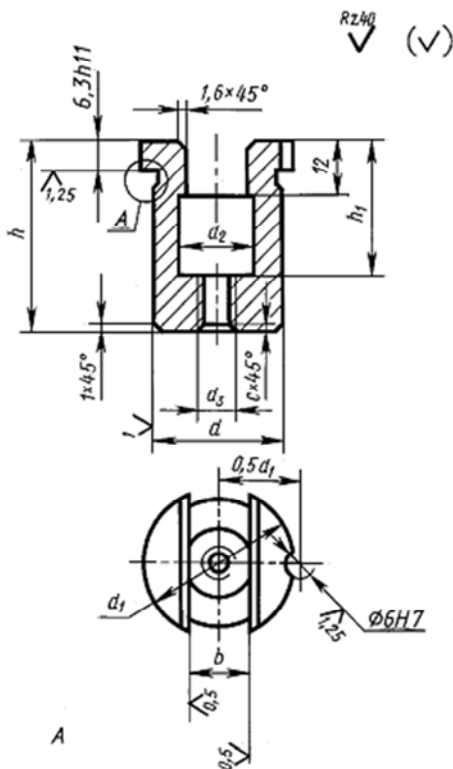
Конструкция направляющих втулок с резьбовым отверстием и отверстием под фиксатор
